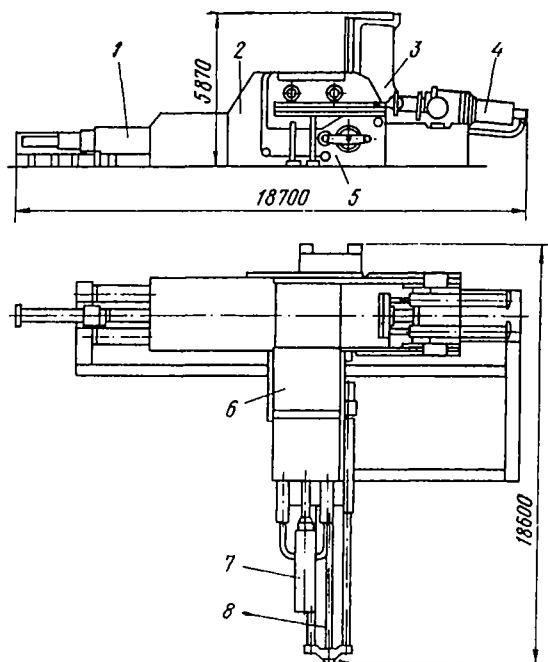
Пакетировочный гидравлический пресс Б 1642
